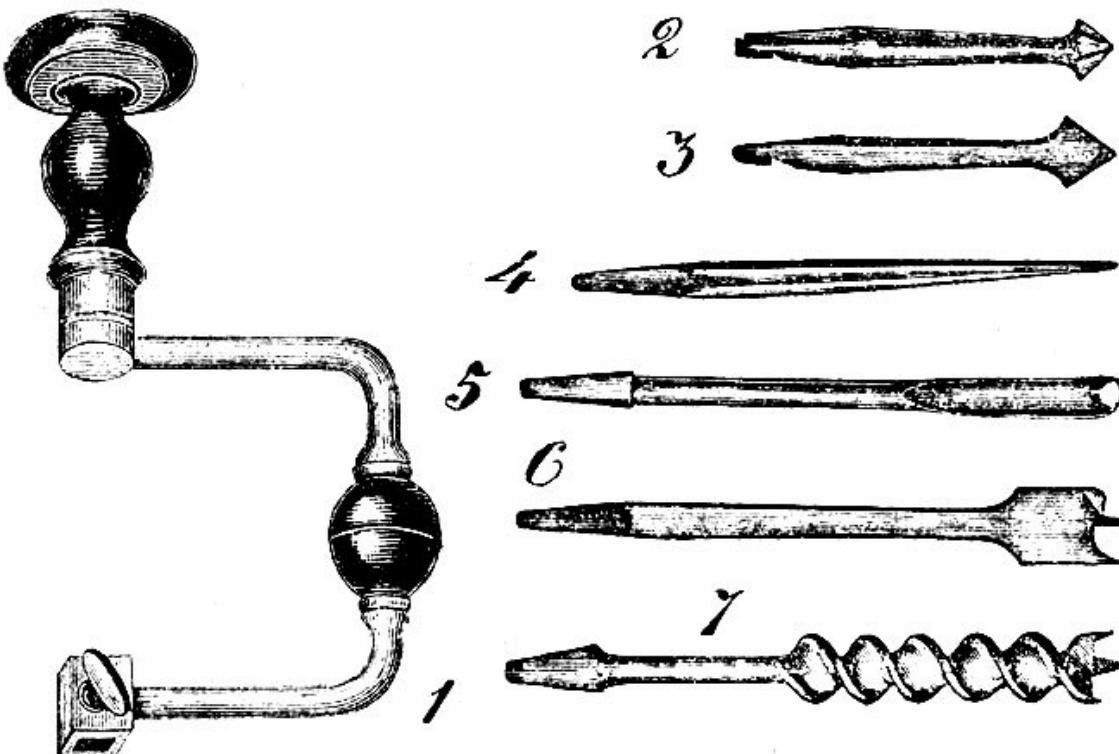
Фиг. 1 – коловорот; 2 и 3 – зенковки; 4 – граненое шило; 5 – ложечная перка; 6 – центровая перка; 7 – спиральное сверло
